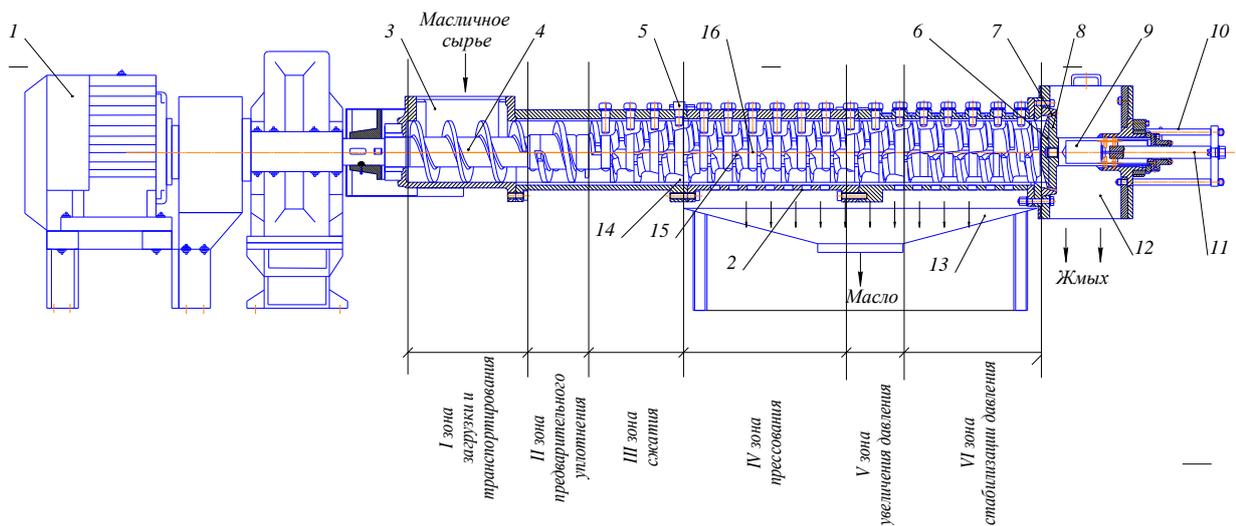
Маслопресс: 1 – привод, 2 – зерные пластины, 3 – загрузочный бункер, 4 – комбинированный шнек, 5 – регулировочные болты, 6 – опорный рассекатель, 7 – выходной зазор, 8 – матрицу, 9 – поршень, 10 – устройство для регулирования величины выходного зазора; 11 – регулировочный шток, 12 – разгрузочная камера для выхода жмыха, 13 – выгрузочный лоток, 14 – рабочая камера
